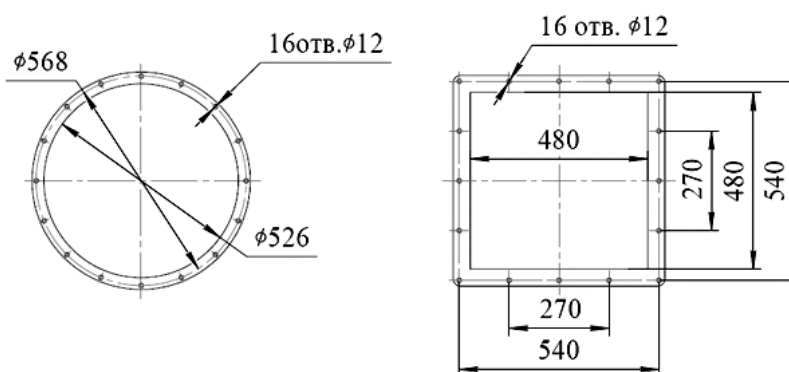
Вентиляторы ВРП-115-49-8. Присоединительные размеры
